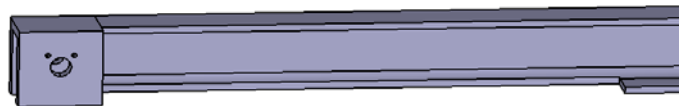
Unión entre la pieza soporte superior y el perfil UPE 80 superior
